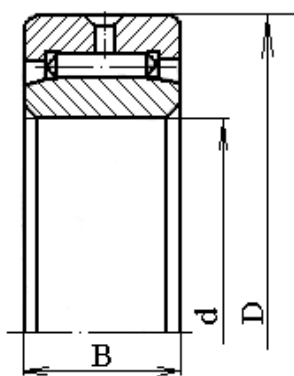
Подшипник роликовый радиальный с длинными цилиндрическими роликами
